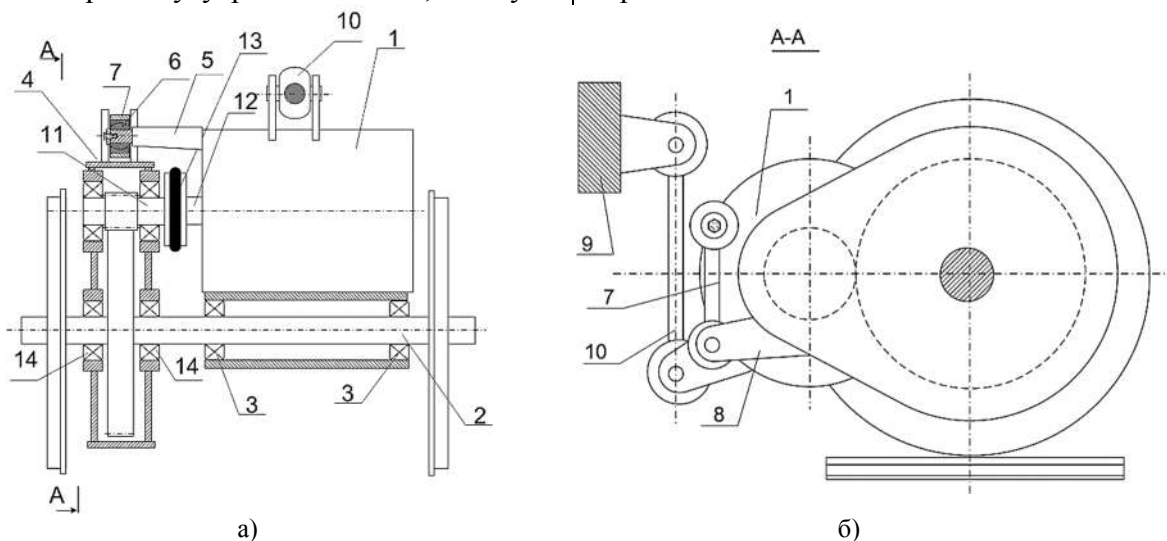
Агрегатная компоновка опорно-осевого привода: а) общий вид; б) вид со стороны осевого редуктора; 1 – ТЭД; 2 – колесная пара; 3,14 – подшипники; 4 – осевой редуктор; 5 – кронштейн с пальцем; 6 – сферический шарнир; 7 – подвеска; 8 – кронштейн осевого редуктора; 9 – рама тележки; 10 – подвеска ТЭД; 11 – вал ТЭД; 12 – вал осевого редуктора; 13 – упруго-компенсационная муфта
